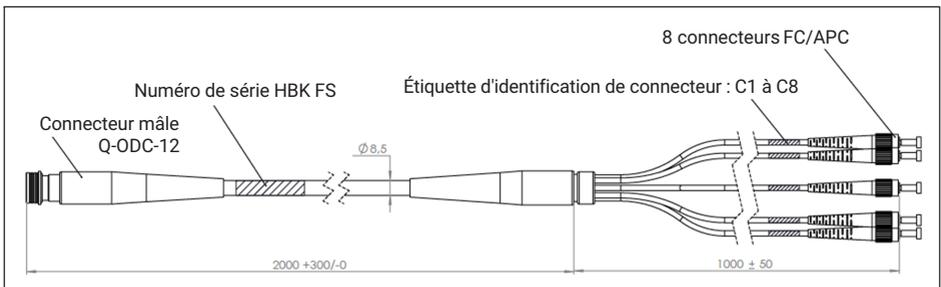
Dessin technique du câble de liaison (dimensions en mm)
